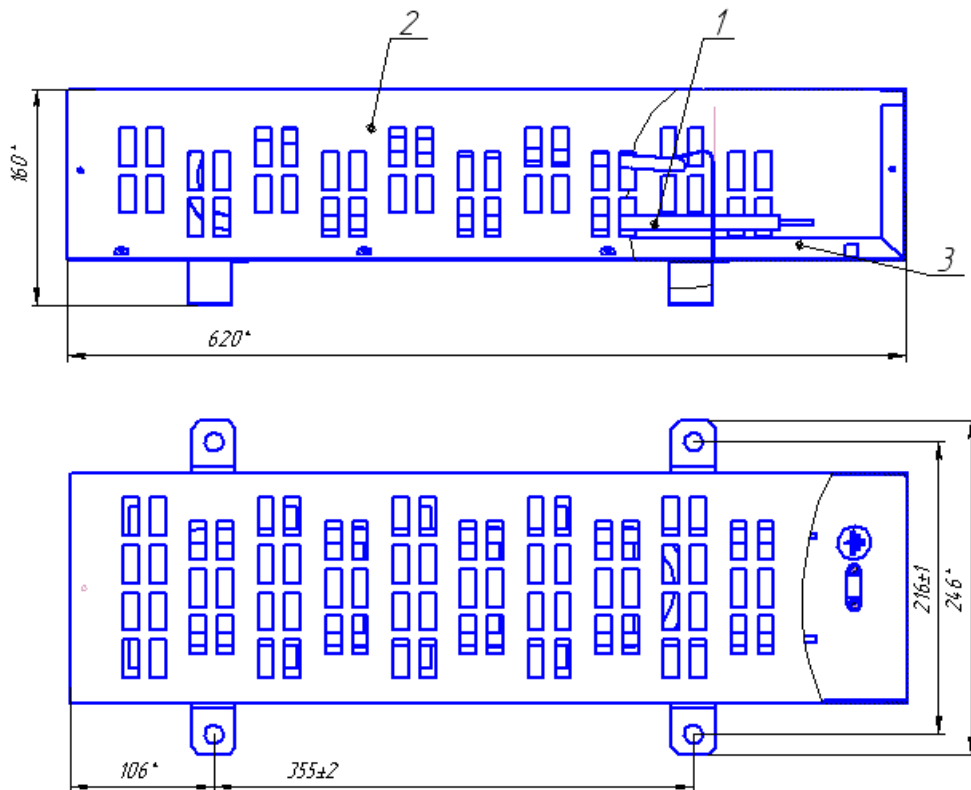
Габаритные и присоединительные размеры электрообогревателей ПЭТ.
